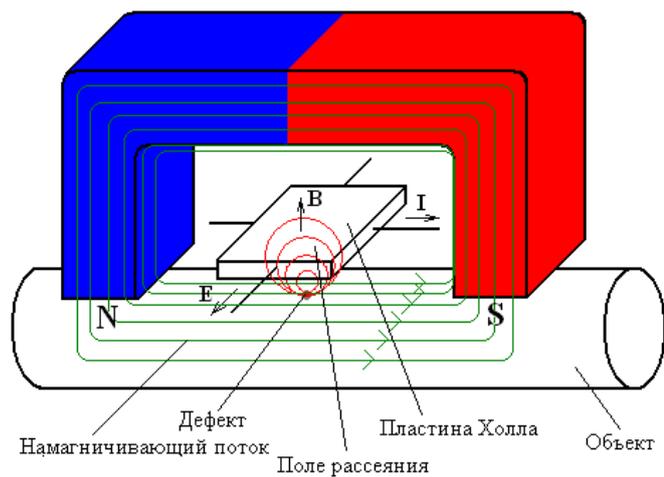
Схематическое представление конструкции магнитной головки прибора для контроля изделий методом Холла
